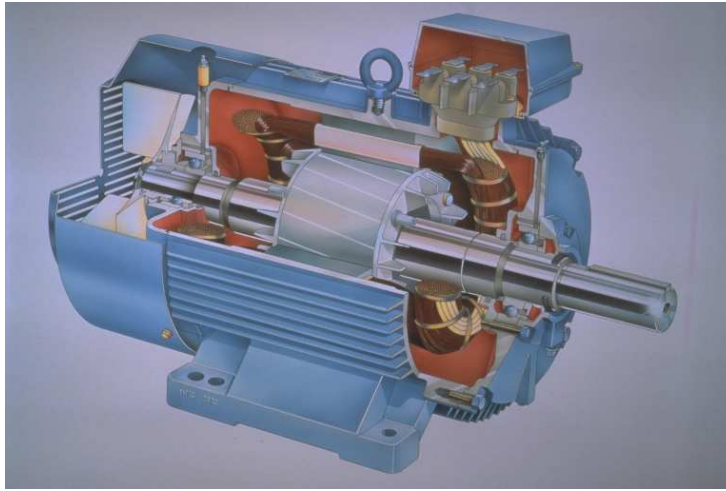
Corte de una máquina de inducción con rotor de jaula de ardilla
